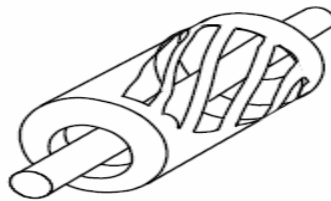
Rotor d'un moteur à cage d'écureuil [13]
